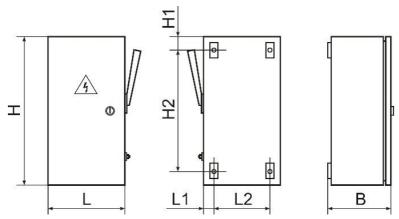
Общий вид и габаритные размеры ящиков силовых
